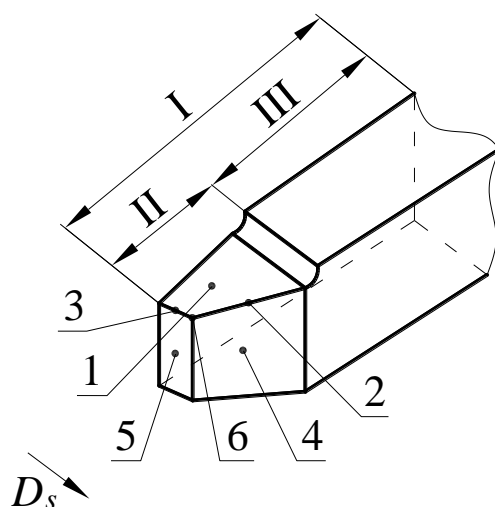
Конструктивные элементы токарного резца: I — корпус резца; II — рабочая часть; III — крепежная часть; 1 — передняя поверхность; 2 — главная режущая кромка; 3 — вспомогательная режущая кромка; 4 — главная задняя поверхность; 5 — вспомогательная задняя поверхность; 6 — вершина резца с радиусом закругления вершины лезвия  $r_b$
